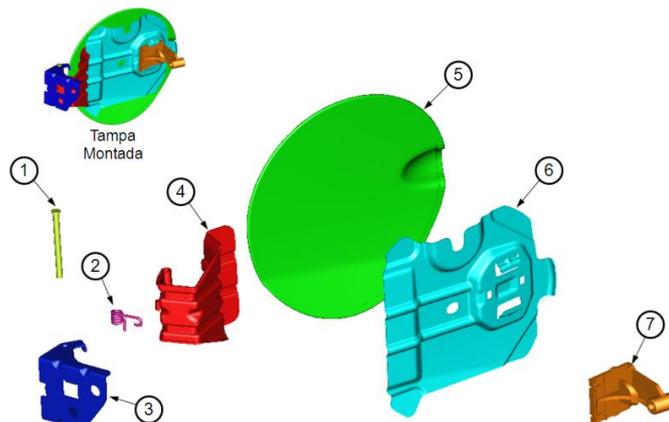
Vista explodida da tampa de combustível na condição inicial de projeto
